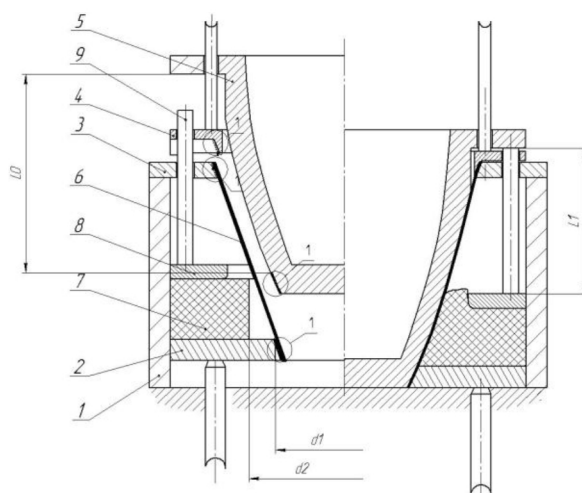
Схема устройства для реализации способа отбортовки-формовки с эластичным элементом
